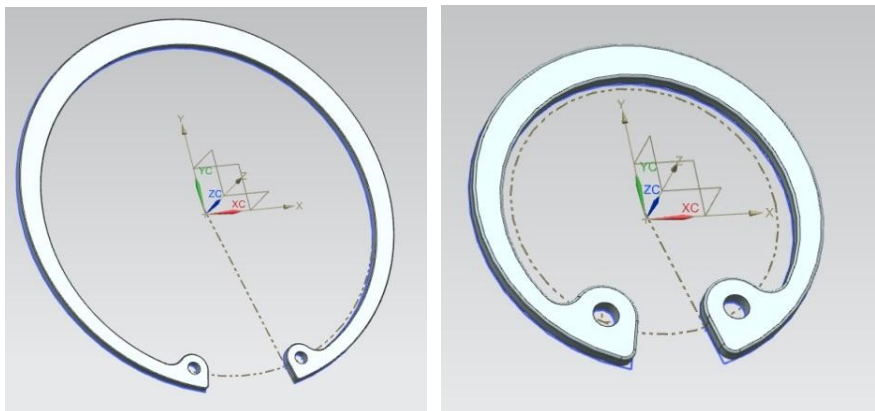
Детали, полученные из параметрической CAD 3D модели стопорного кольца
